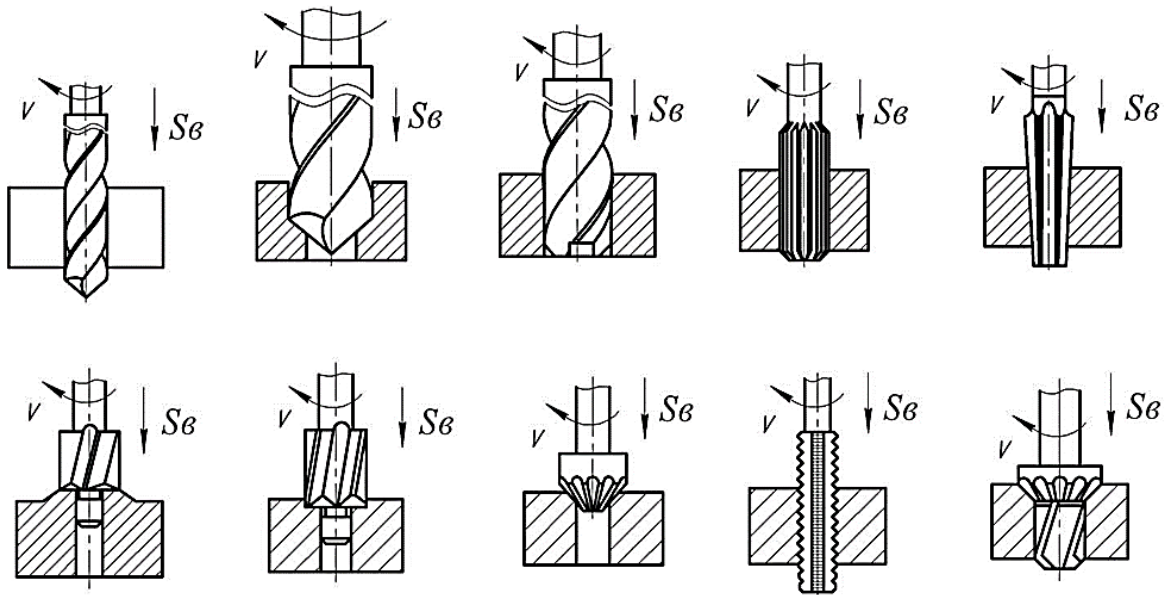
Схеми обробки заготовок на свердлильних верстатах
